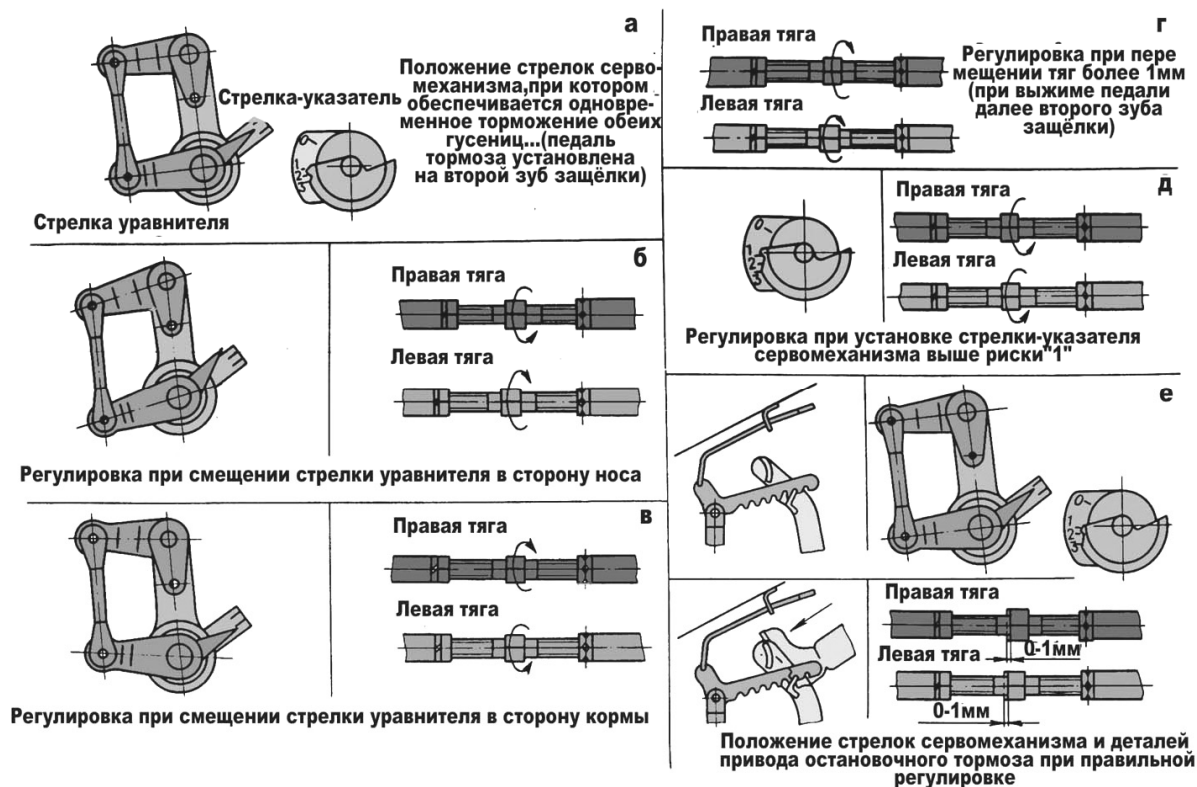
Регулировка привода остановочного тормоза (положение деталей привода при регулировке)
